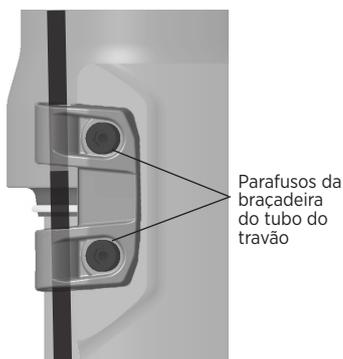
Instalação dos parafusos da braçadeira do tubo do travão
